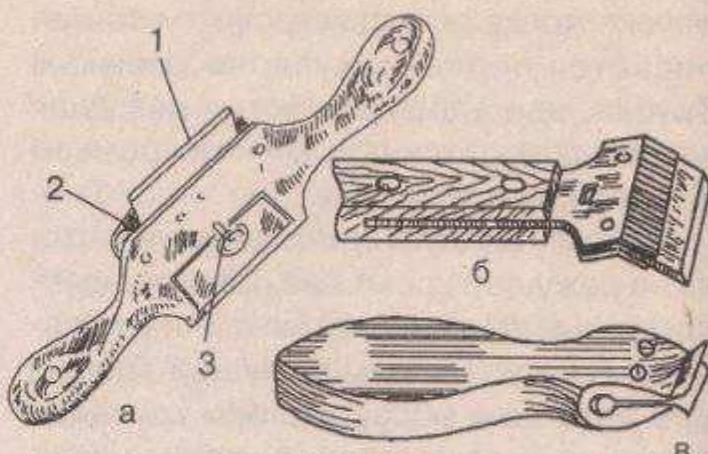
Цикли: а — столярная рубаночного типа; б — паркетная; в — двухсторонняя с двумя загнутыми лезвиями; 1 — нож; 2 — прижимная планка; 3 — регулировочный винт с барабашком
